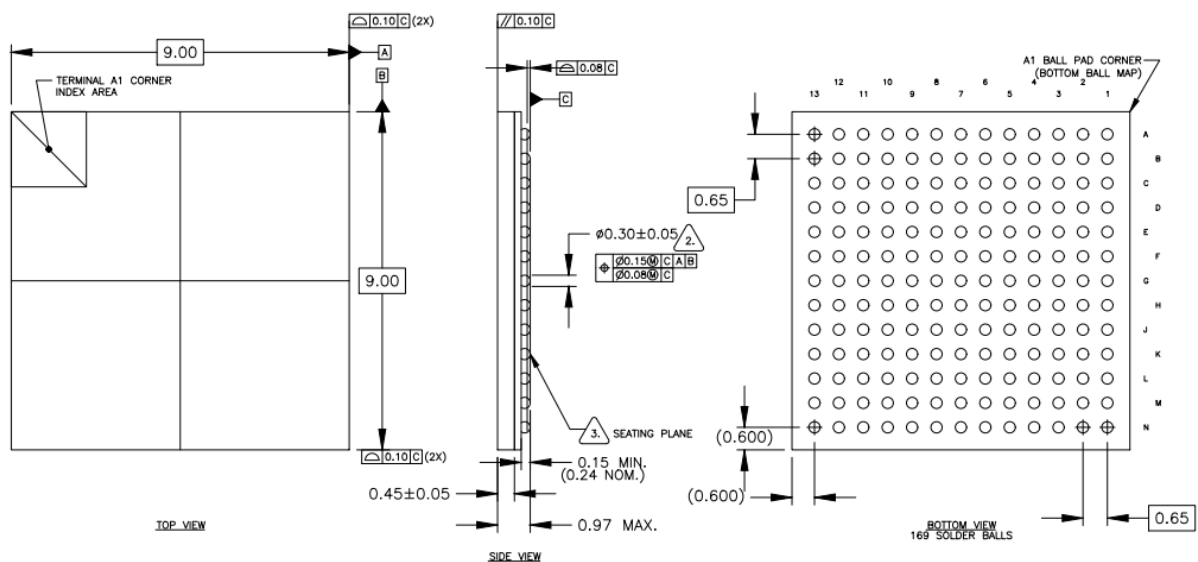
MH1903 BGA169 9mm x 9mm 封装尺寸
